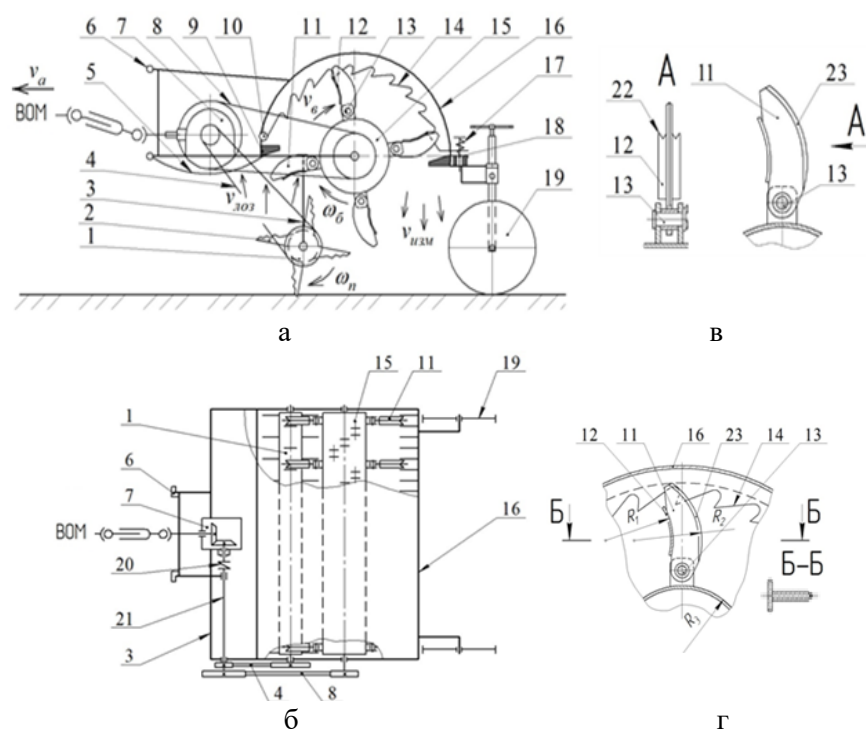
Схема конструктивная подборщика-измельчителя обрезков виноградной лозы: а – вид сбоку, б – вид сверху,
